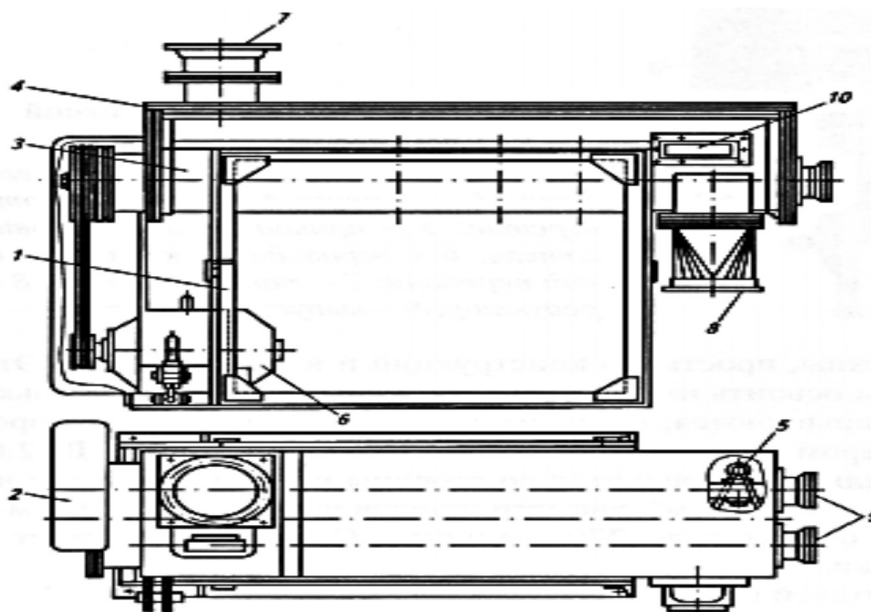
Смеситель МСН: 1 – станина; 2 – редуктор; 3, 5 – шнеки; 4 – крышка; 6 – электродвигатель; 7, 8 – приемный и выпускной патрубки; 9 – подшипниковые опоры; 10 – смотровое окно
